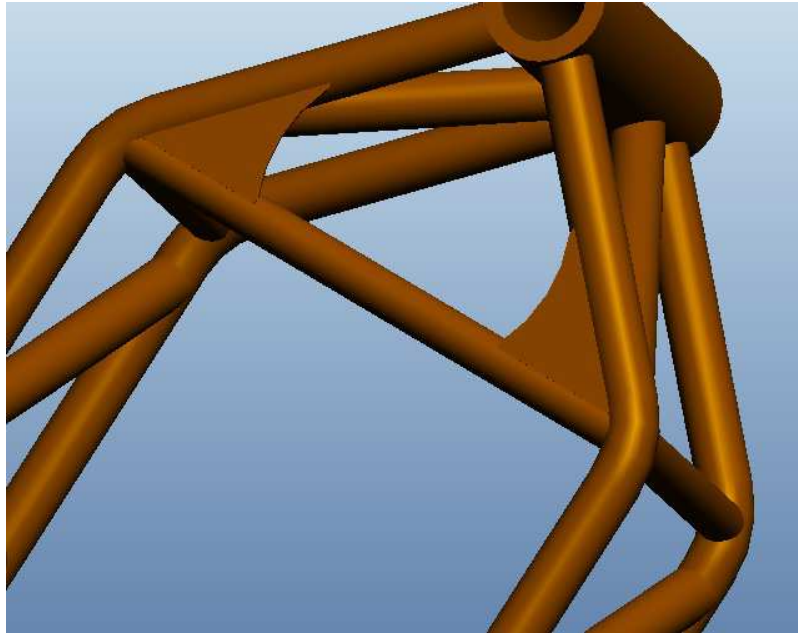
Detalles de los refuerzos en el travesaño del prototipo B
